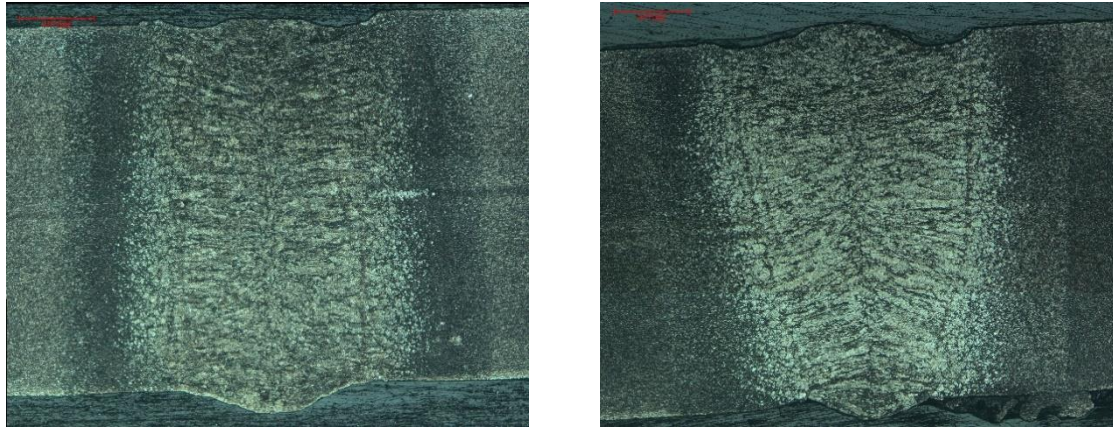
Perfil longitudinal do cordão de soldadura da amostra 7.
